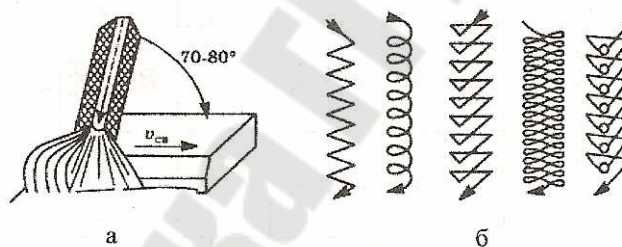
Положение (а) и поперечное движение (б) электрода при сварке нижних стыковых швов
